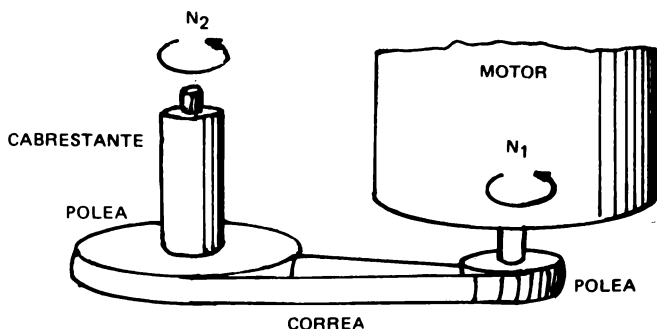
Disposición esquemática de la transmisión del movimiento del motor al resto del mecanismo mediante poleas y correas.
